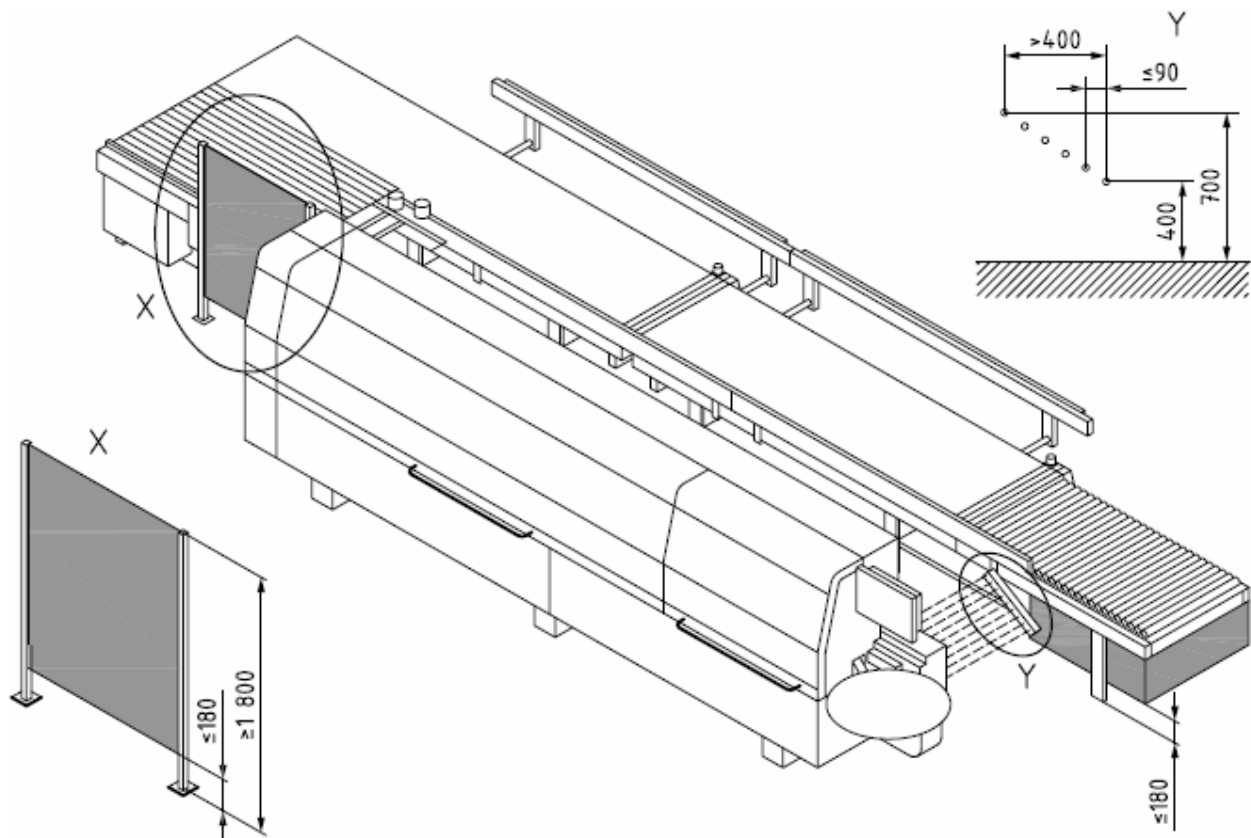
Пример автоматического устройства возврата заготовки с AOPD на одностороннем станке
